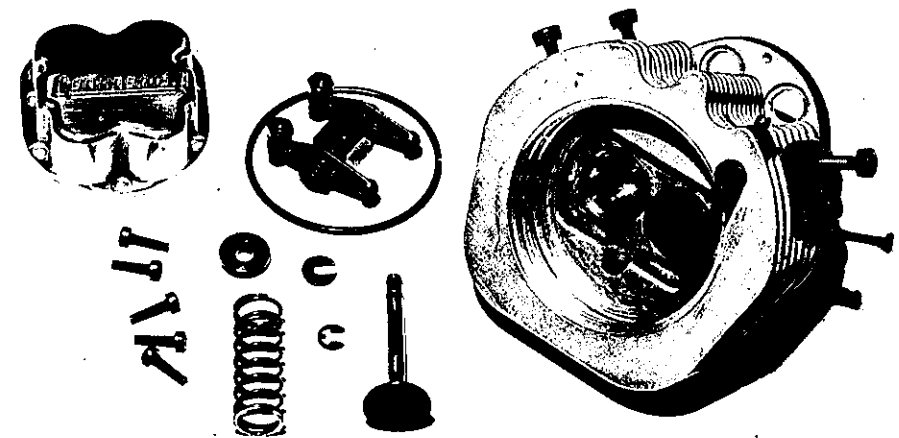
Anordnung der beiden parallel stehenden Ventile im Zylinderkopf des FK-50-Boxermotors. Der Zylinderkopf ist auf den Zylinder mit Gewinde aufgeschraubt. Ein temperaturfester Gummiring dichtet den Zylinderkopf gegen die Zylinderbüchse ab. Deutlich ist der Wannenbrennraum um die Ventile zu erkennen.
